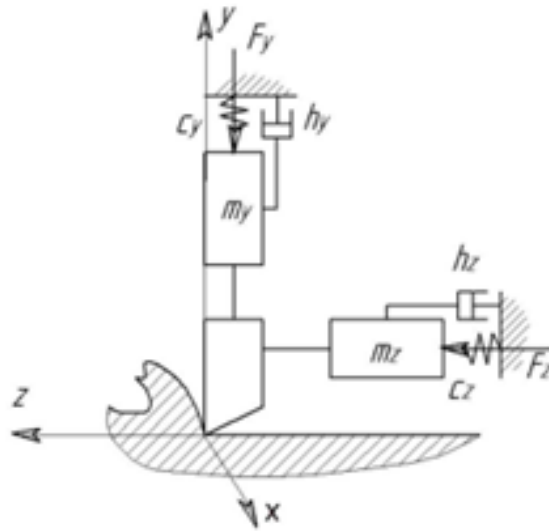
Модель торцевого фрезерування при різанні одним зубом
